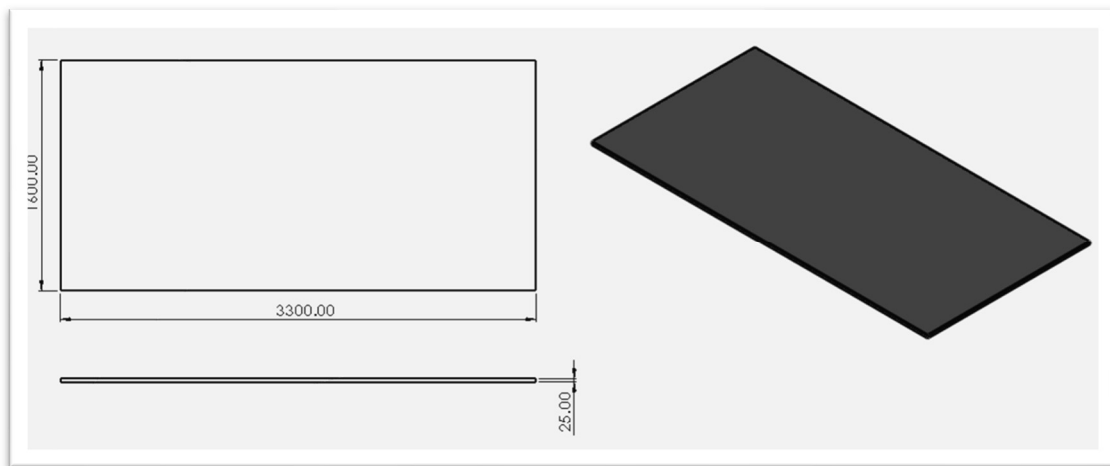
Plancha goma eva - Multigreen. Fuente: Elaboración propia
